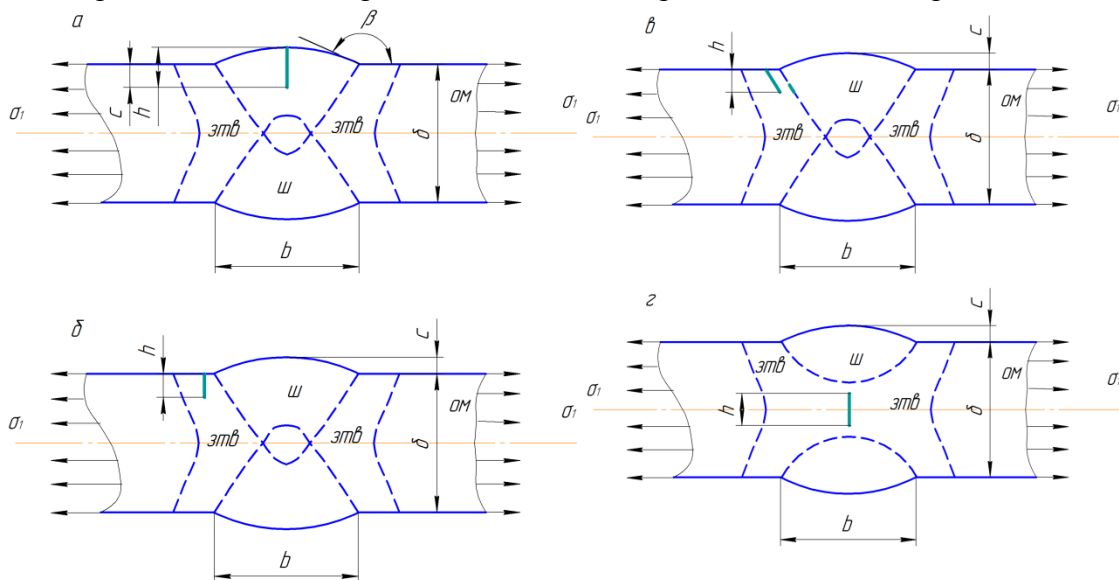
Трещины в сварных двухсторонних стыковых соединениях. ЗТВ - зона термического влияния; Ш - шов; ОМ - основной металл; h - размер трещины; b - ширина шва; C - высота усиления шва; δ - толщина конструкции.
